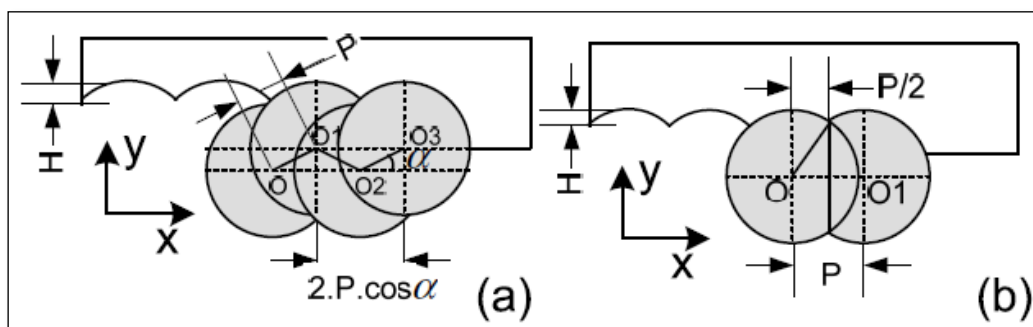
Schéma de principe des passages d'un outil d'usinage
